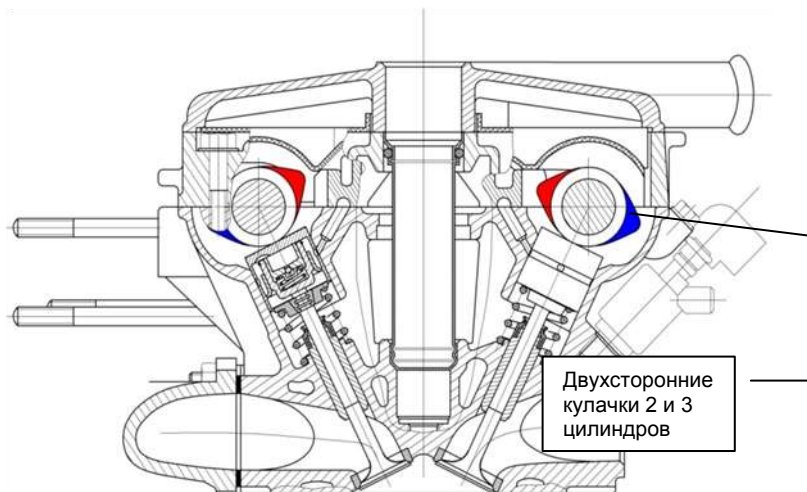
Измененная головка цилиндров двигателя ВАЗ
